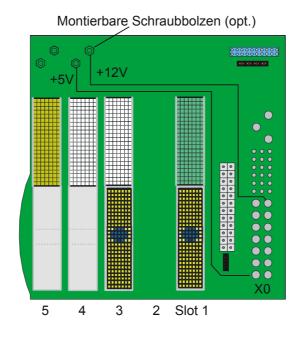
Montierbare Schraubbolzen auf der cPCI-Backplane
